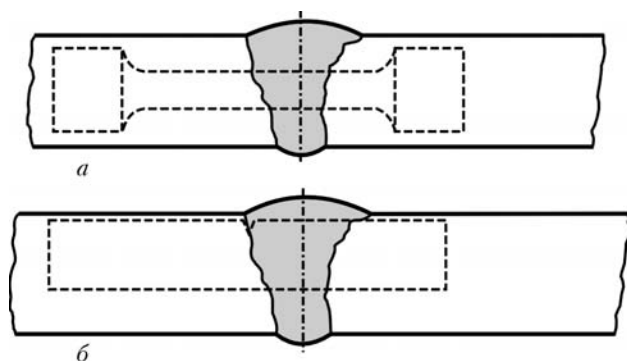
Схема вырезки из темплетов сварных соединений образцов типа II (а) и IX (б) для механических испытаний
